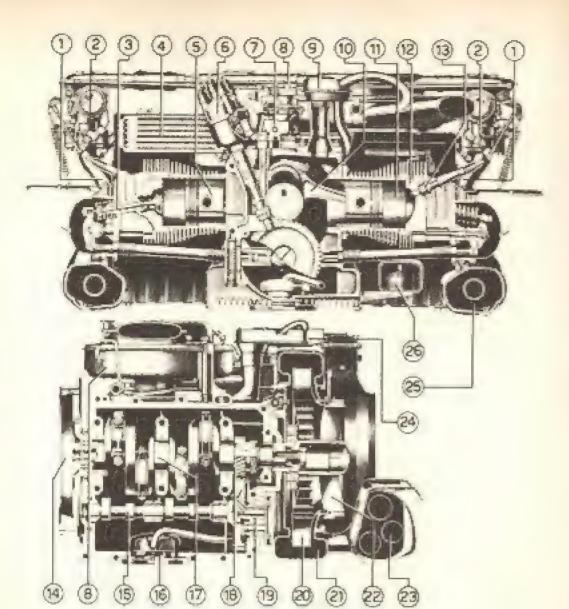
V - O motor plano "1 600" visto em dois cortes
